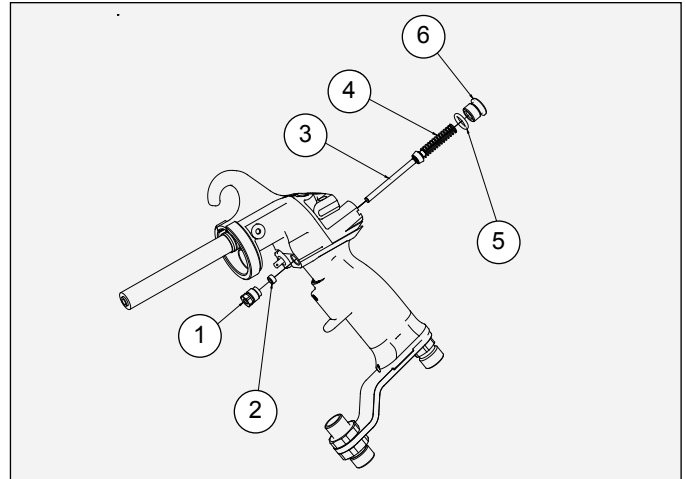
Dépose du chapeau de retenue de vanne d'air et du joint torique
